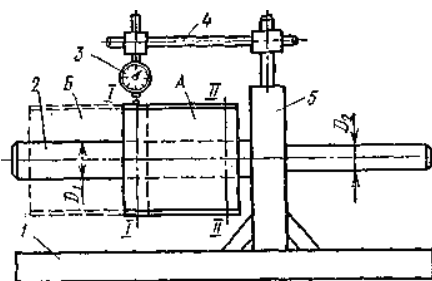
Контрольно-настановне пристосування для зборки фрез невеликого розміру: 1 — основа, 2 — оправлення, 3 – індикатор, 4 — штатив, 5 — стійка
